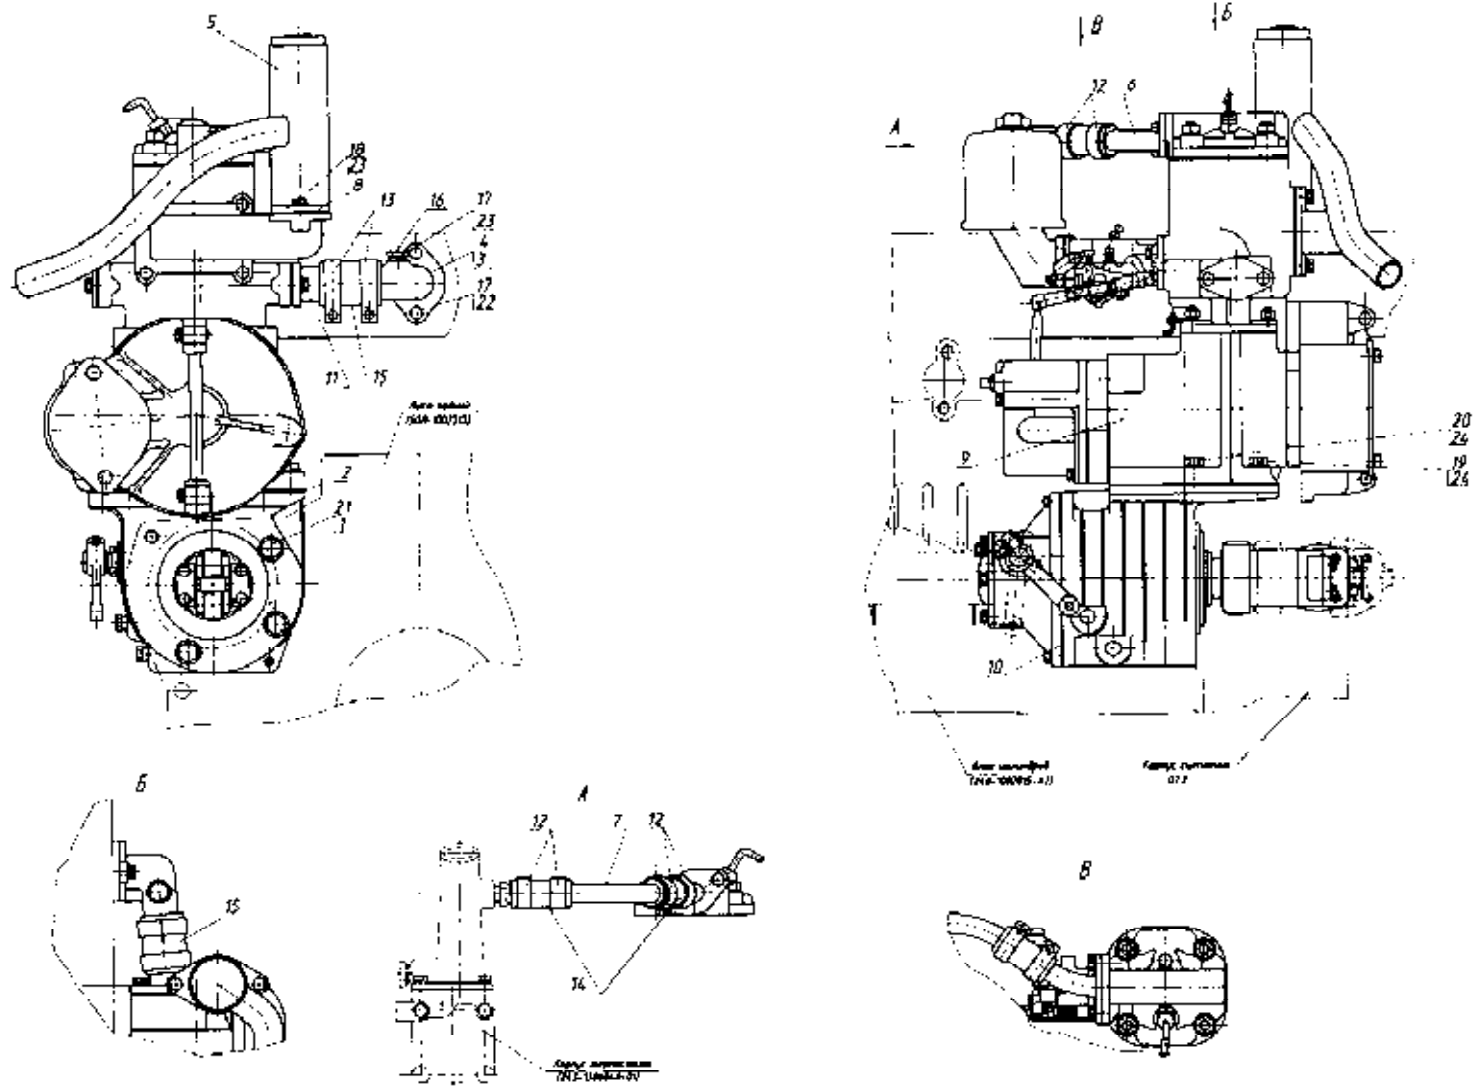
Установка пускового двигателя (для двигателя Д-245.16ЛС).
